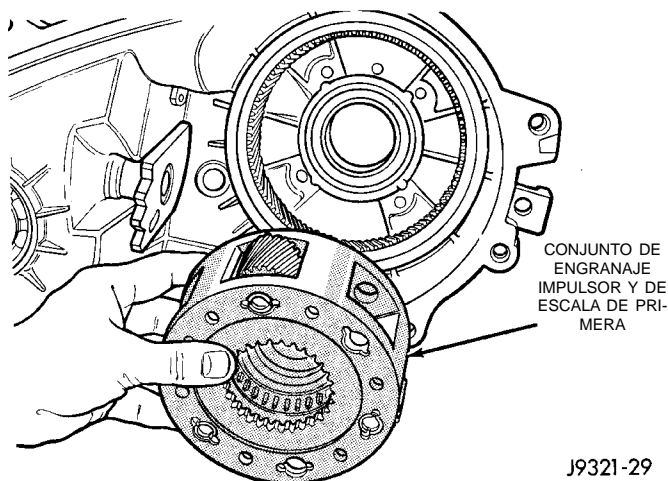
Desmontaje del conjunto del engranaje impulsor y de escala de primera
